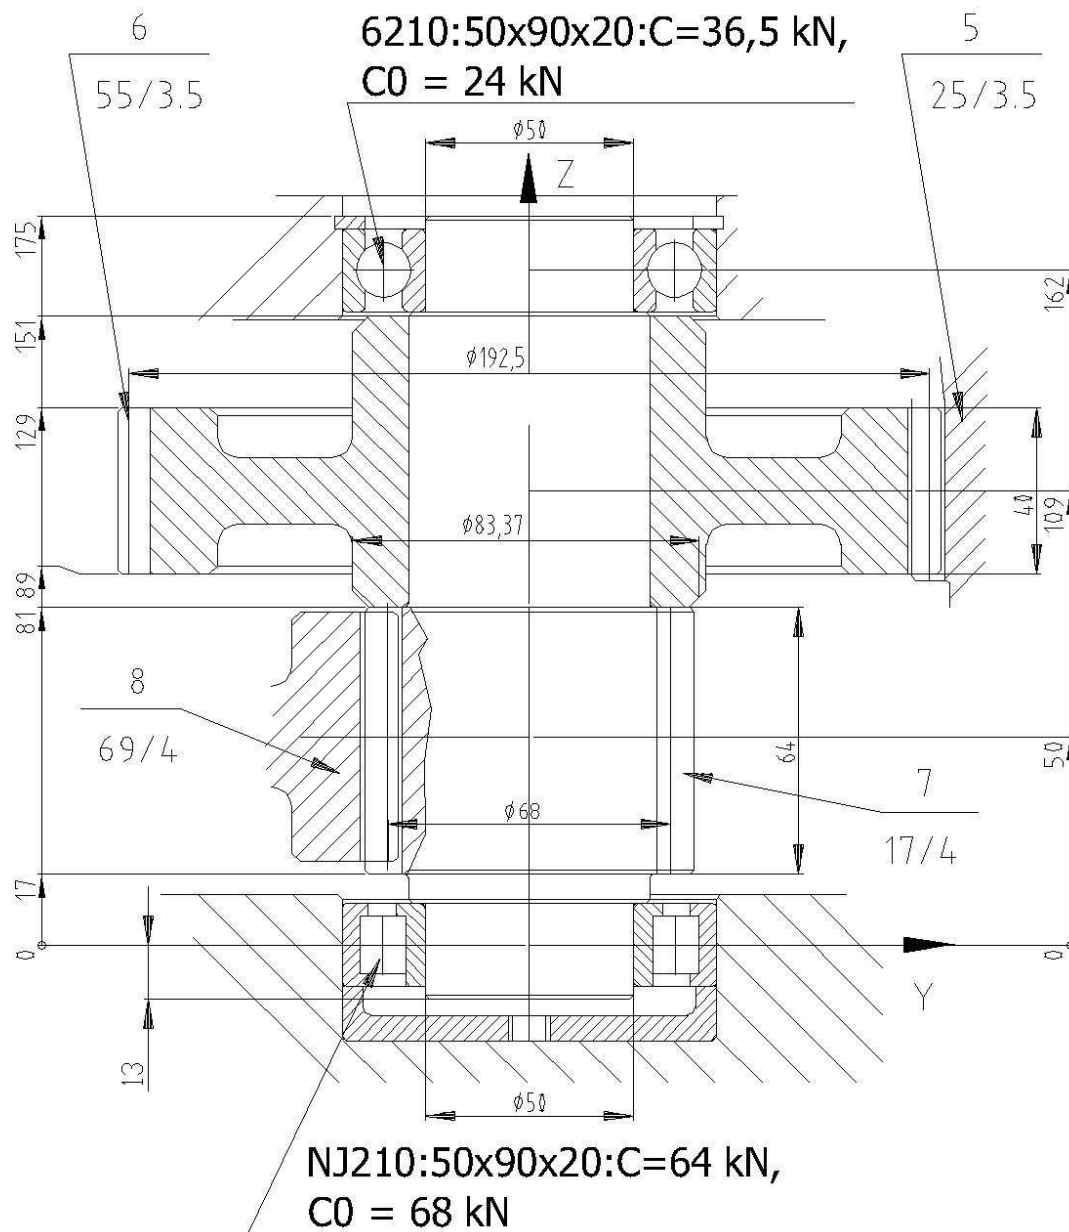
Posuvová skříň se dvěma předepnutými pastorky [12]
